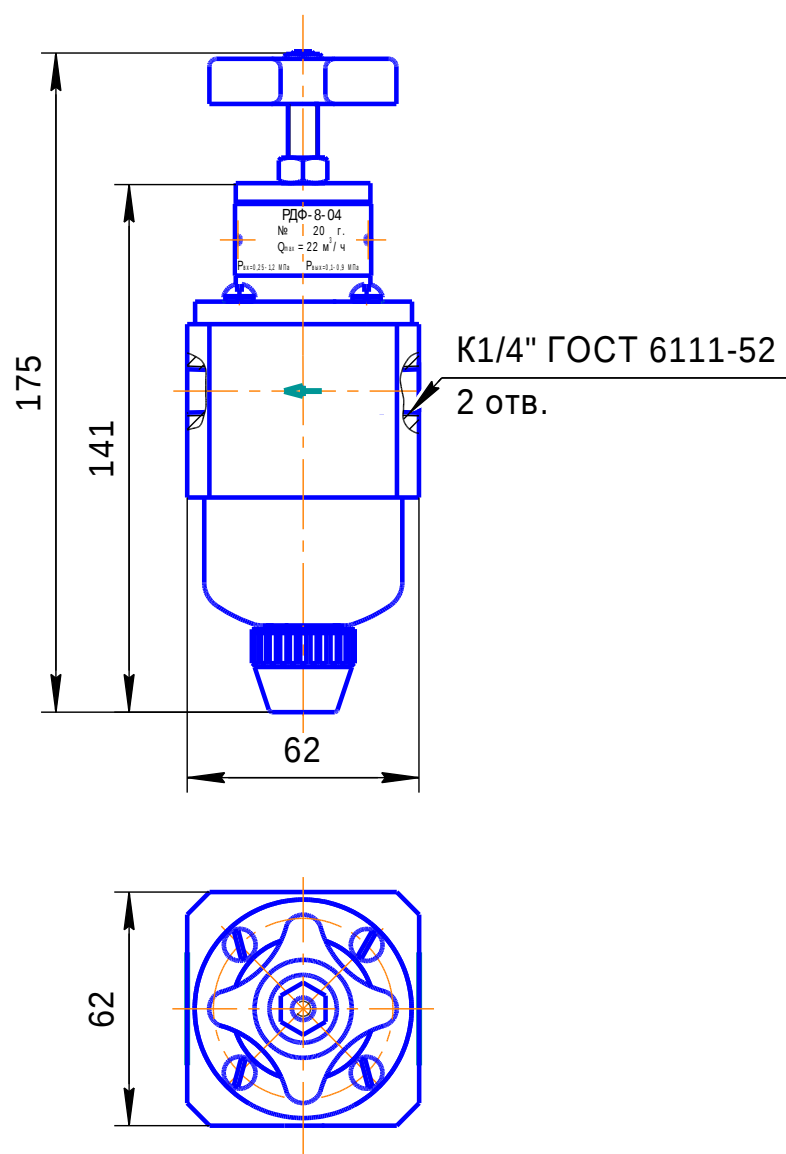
Габаритные и присоединительные размеры редуктора РДΦ-8-04
